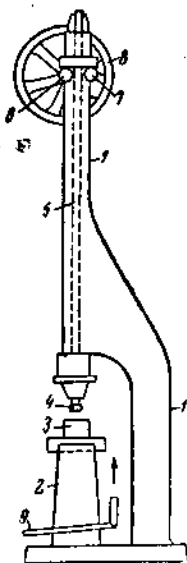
Схема камнекольной машины: 1 — станина; 2 — наковальня; 3 — боек наковальни; 4 — боек молотка; 5 — рейка; 6 и 7 — ролики; 8 — шкив; 9 — педаль
